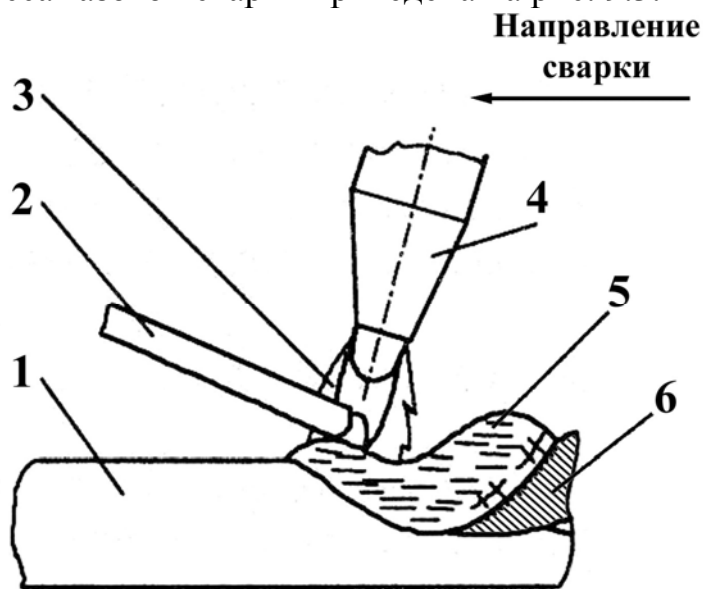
Схемы процесса газовой сварки:
